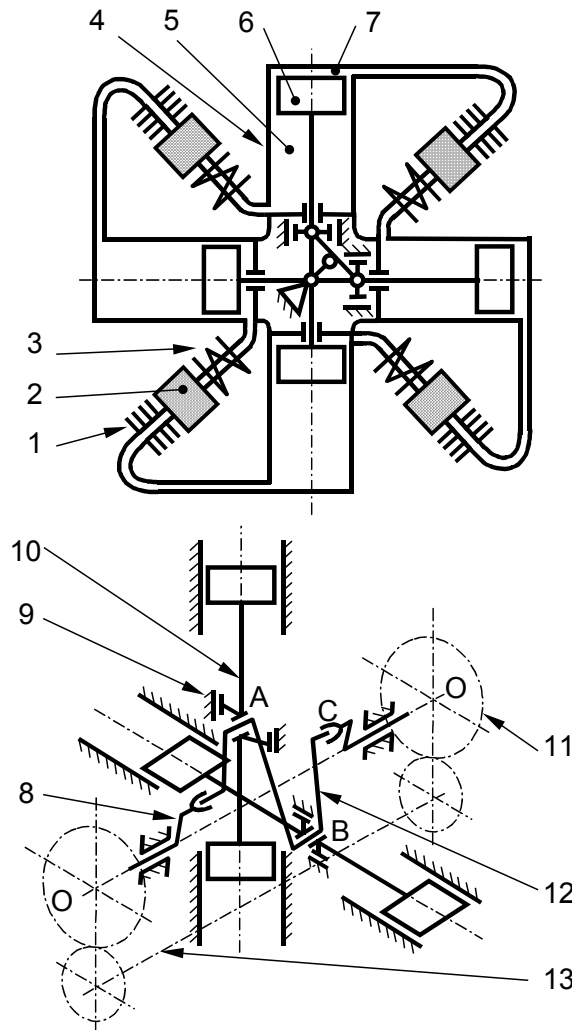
Motor Stirling cu pistoane cu dublă acțiune și cu mecanism motor Balandin: 1 - încălzitor; 2 - regenerator; 3 - răcitor; 4 - cilindru; 5 - cameră de comprimare; 6 - piston; 7 - cameră de destindere; 8 - manivelă; 9 - glisieră; 10 - tija care solidarizează pistoanele opuse; 11 - roți dințate pentru sincronizare; 12 - arbore cotit; 13 - arbore de sincronizare
